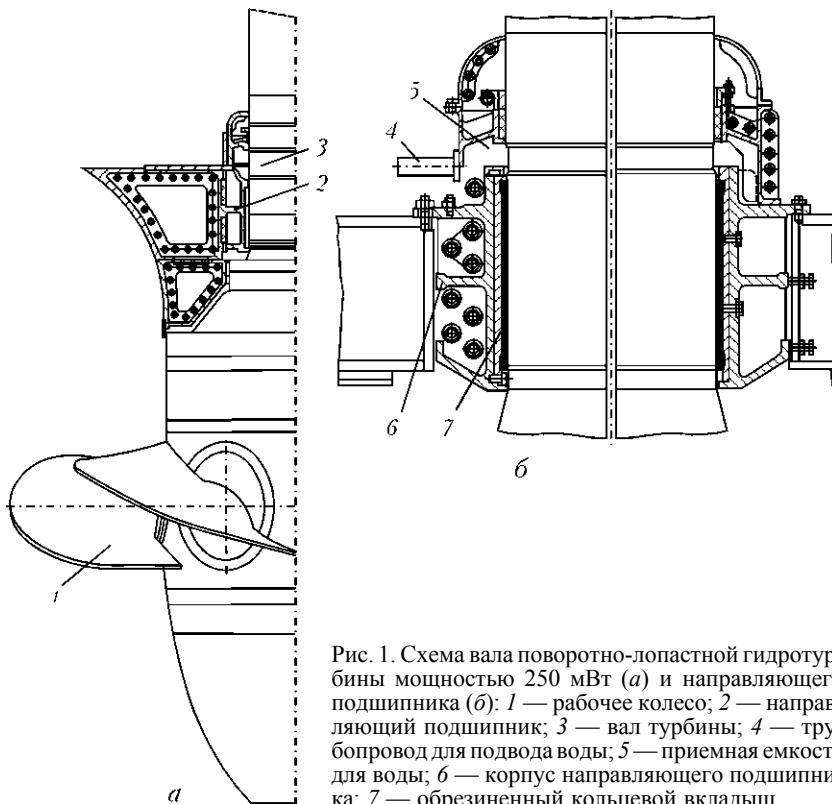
Схема вала поворотного-лопастной гидротурбины мощностью 250 мВт (а) и направляющего подшипника (б): 1 — рабочее колесо; 2 — направляющий подшипник; 3 — вал турбины; 4 — трубопровод для подвода воды; 5 — приемная емкость для воды; 6 — корпус направляющего подшипника; 7 — обрешиненный кольцевой вкладыш
